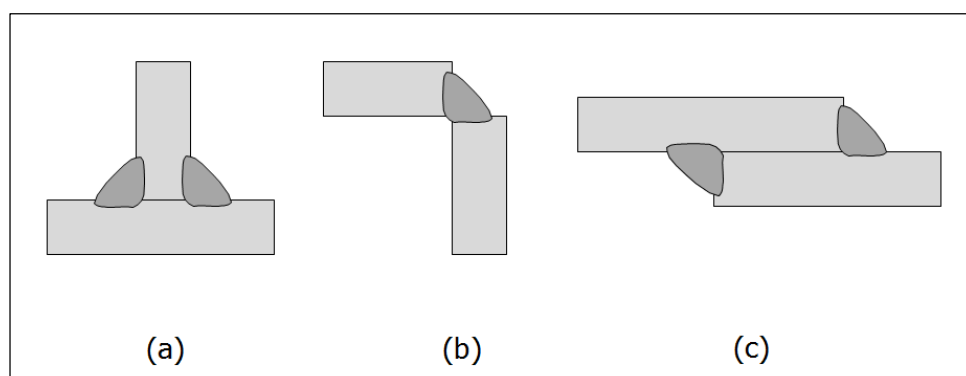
Ejemplos de soldaduras de tipo filete
